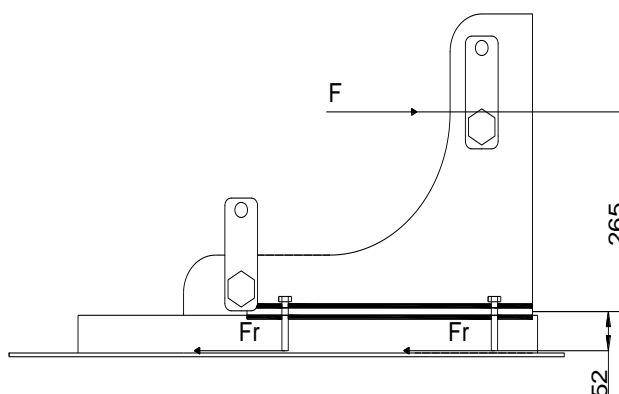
2: Esquema de las fuerzas actuantes sobre la soldadura
